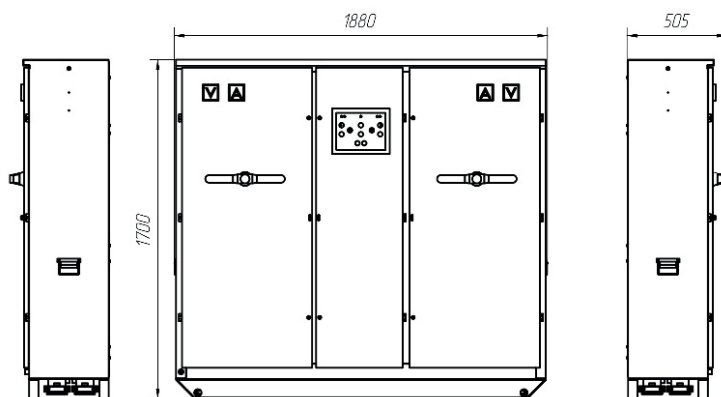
Конструкция шкафа АВР-2х800...2х1600А
